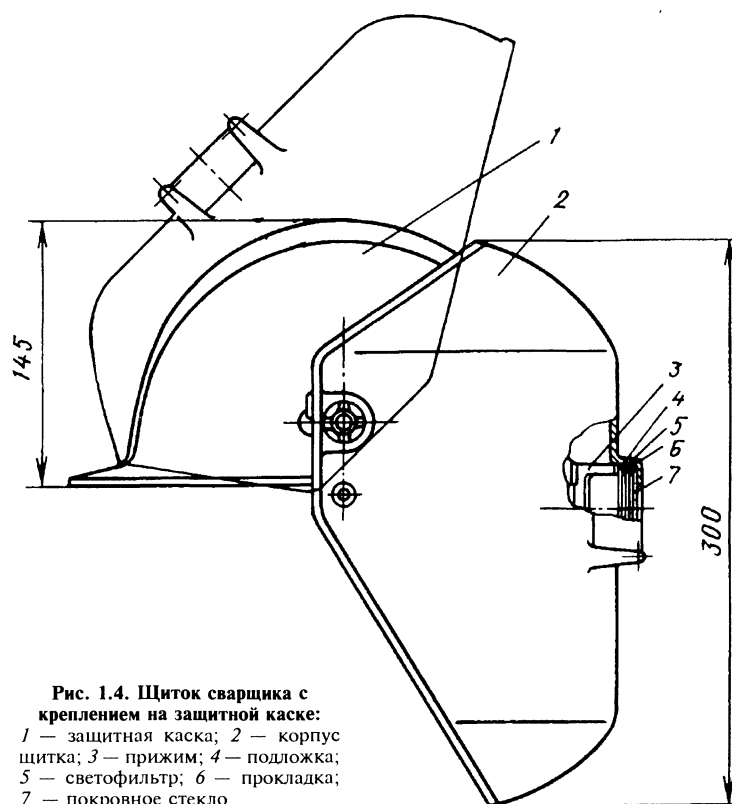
Щиток сварщика с креплением на защитной каске:
